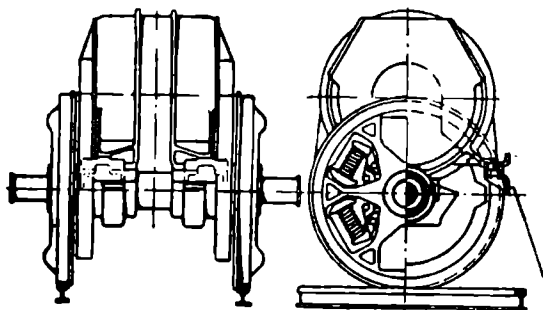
Мотор, расположенный над осью зубчатой передачи.
